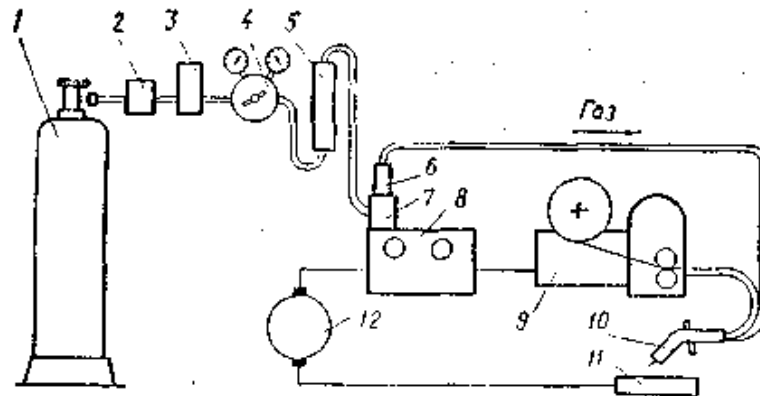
Схема установки для напівавтоматичного зварювання і наплавлення у середовищі вуглекислого газу:
